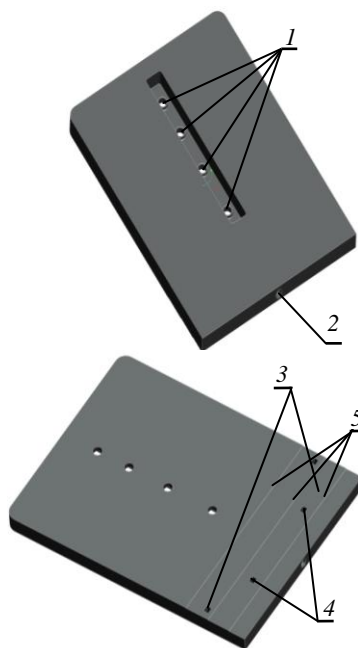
Конструктивные элементы крышки корпуса ИМБ: 1 — отверстия под приварку трубок газа-носителя; 2 — отверстие под установку входного патрубка газа-носителя; 3 — вход газового теплоносителя; 4 — выход газового теплоносителя; 5 — технологические ступеньки под приварку перегородок блока газовых коллекторов
